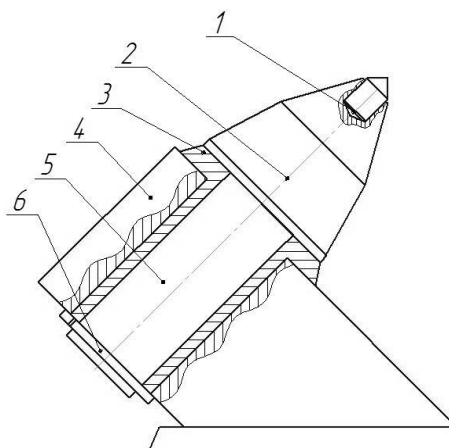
Резец новой конструкции с втулкой в резцедержателе: 1 – твердосплавная вставка; 2 – головка с опорным буртом; 3 – втулка; 4 – резцедержатель (кулак); 5 – хвостовик; 6 – фиксатор.
